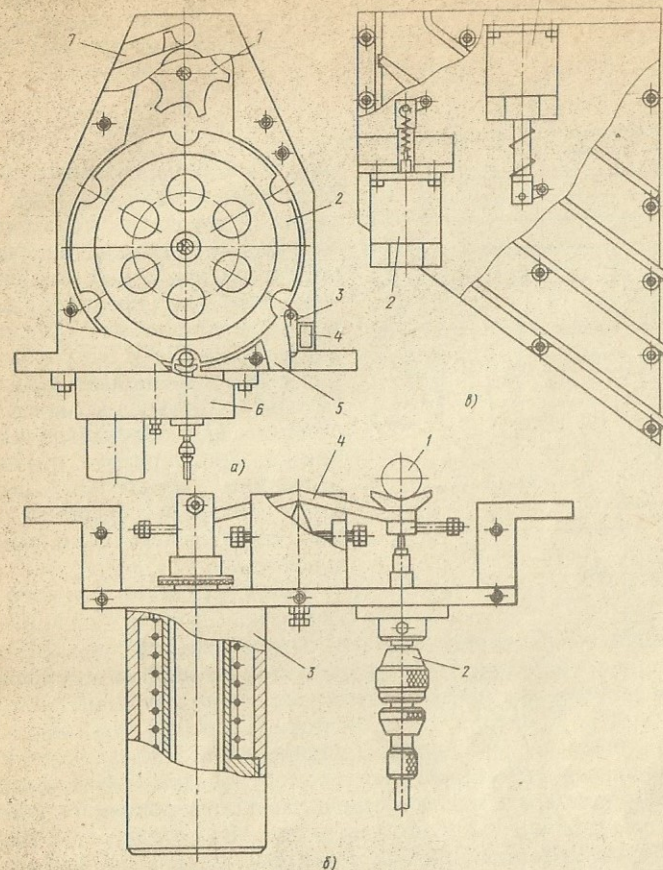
Механизмы автомата для сортировки заготовок поршневых пальцев: а — транспортирования; б — контроля; в — сортировки
